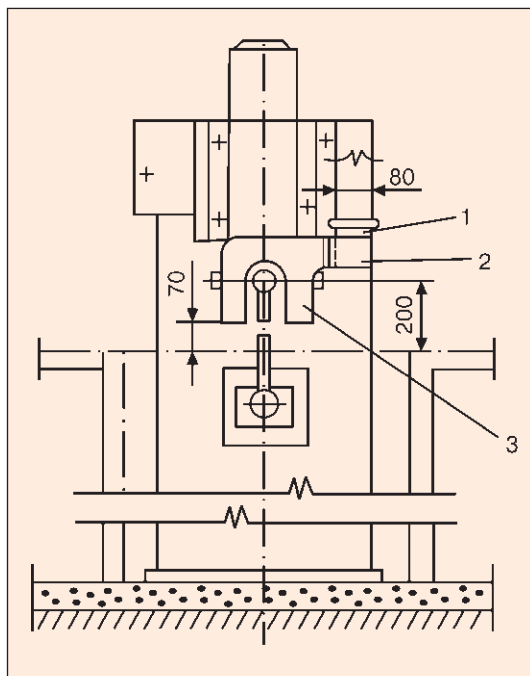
Верхний воздухоприемник к машине для контактной сварки: 1 — шибер; 2 — патрубок; 3 — воздуховод
